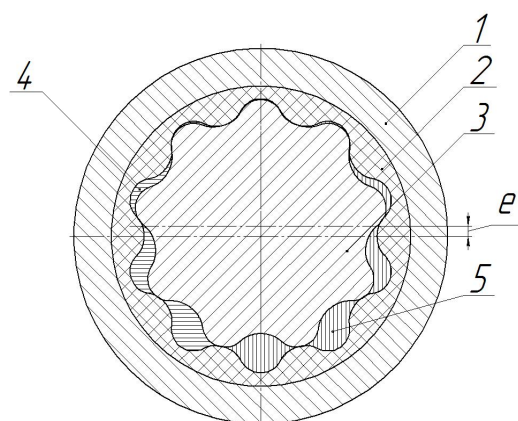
Поперечный разрез двигателя: 1) корпус статора; 2) обойма статора; 3) ротор; 4) камеры низкого давления; 5) камеры высокого давления
